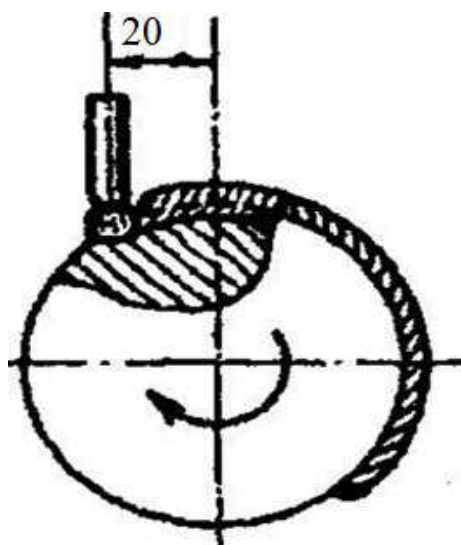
схема наплавки валка двухвалковой дробилки ДГ-400×250.
